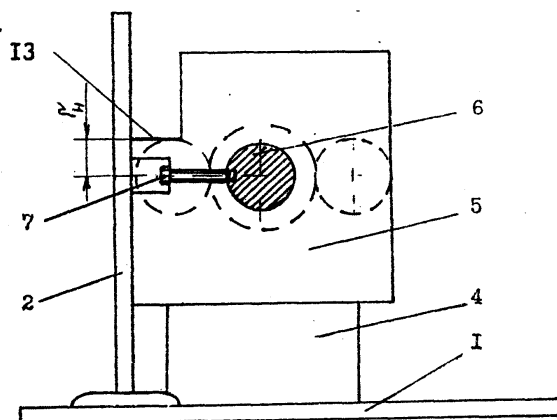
Устройство для измерения углового расположения шатунных шеек коленчатого вала под 180° . (вид сбоку)
